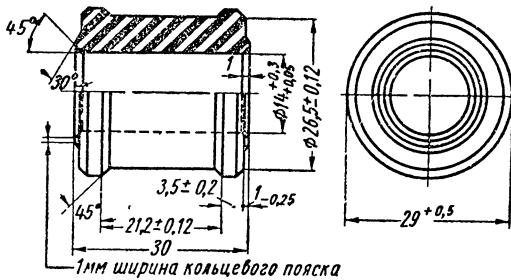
Запрессовка резиновой втулки рычага амортизатора.
